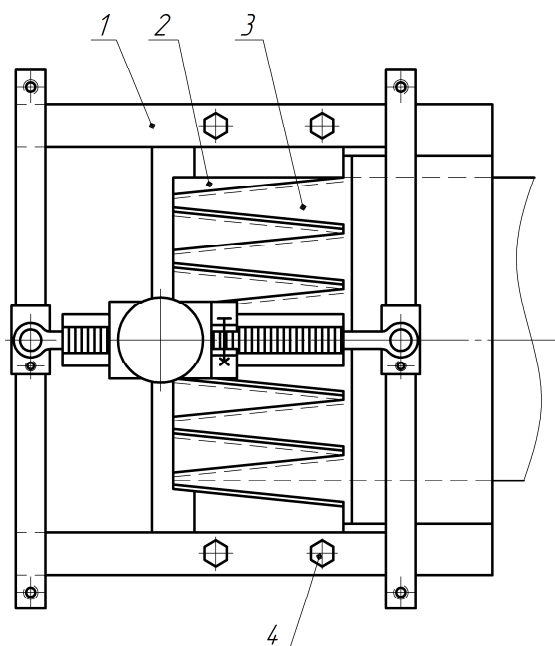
Устройство для разделки концов резиноканевых лент под зубчатый стык
